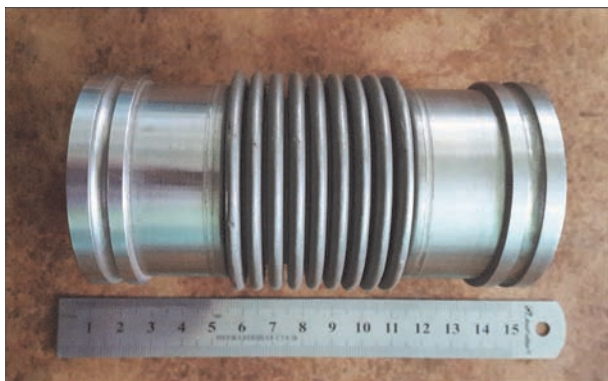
Багатошаровий сиффон, виготовлений з труб, що зварені лазерним випромінюванням
